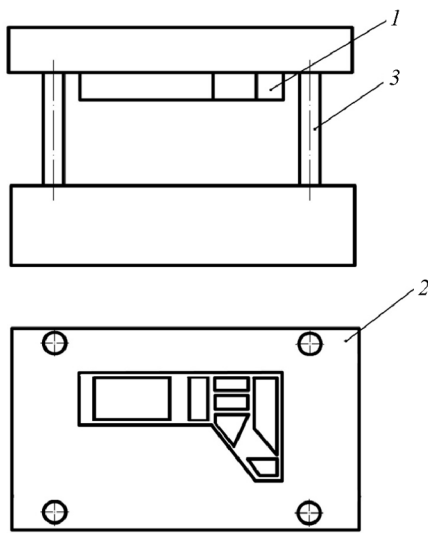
Схема совмещенного штампа для изотермической штамповки
